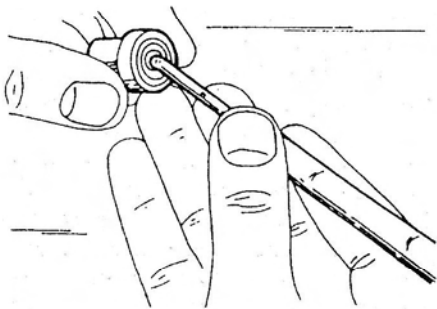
Очистить внутреннюю полость тела форсунки с помощью шпателя для кольцевых углублений.
